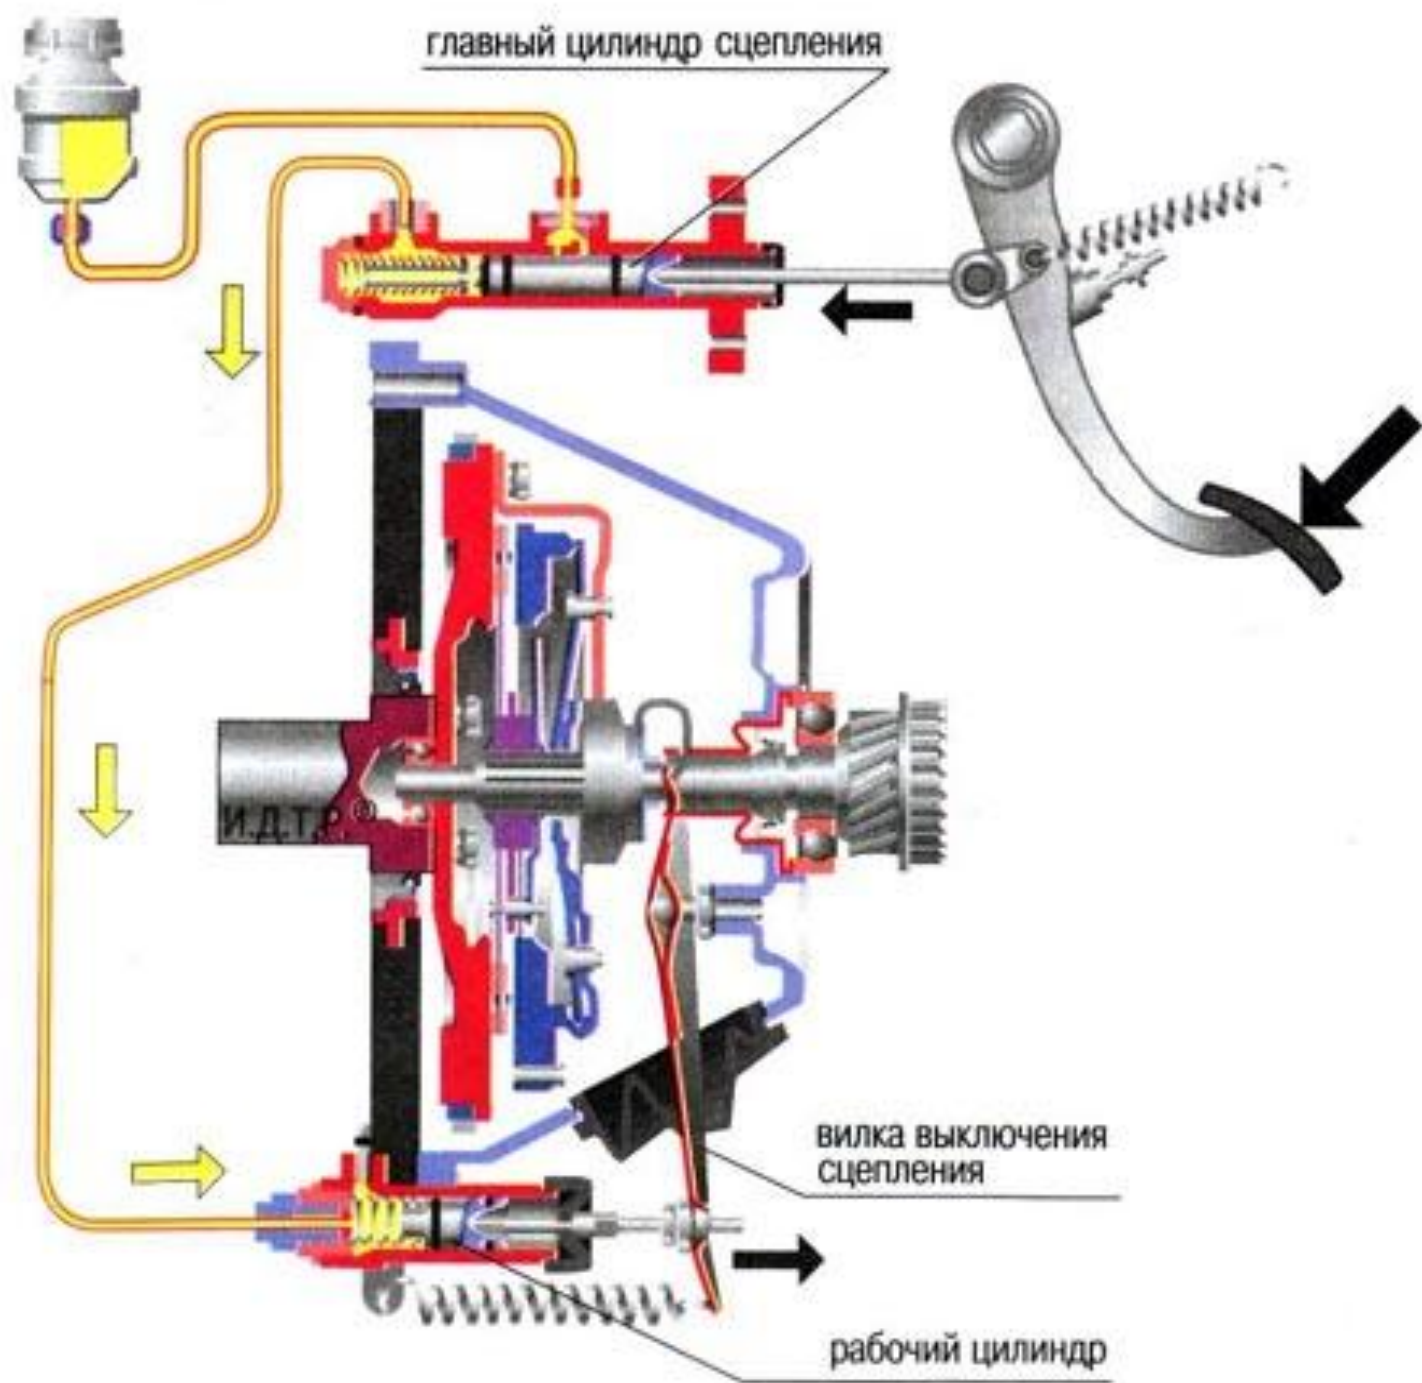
Схема гидравлического привода выключения сцепления и механизма сцепления: 1 – трубопровод; 2 – нажимной диск; 3 – ведомый диск; 4 – маховик; 5 – коленчатый вал; 6 – картер сцепления; 7 – кожух сцепления; 8 – нажимные пружины; 9 – отжимные рычаги; 10 – выжимной подшипник; 11 – первичный вал коробки передач; 12 – шестерня первичного вала; 13 – вилка выключения сцепления; 14 – рабочий цилиндр; 15 – картер коробки передач; 16 – главный цилиндр; 17 – педаль сцепления
